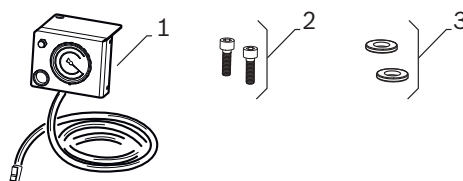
Accessori per il montaggio del manometro di gonfiaggio
